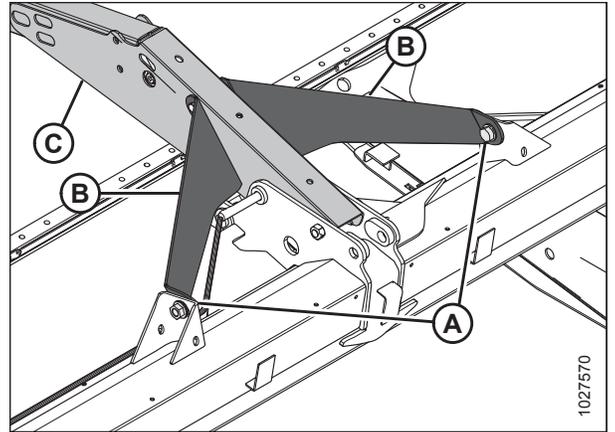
Центральный опорный рычаг мотовила и стяжки – Экспорт
